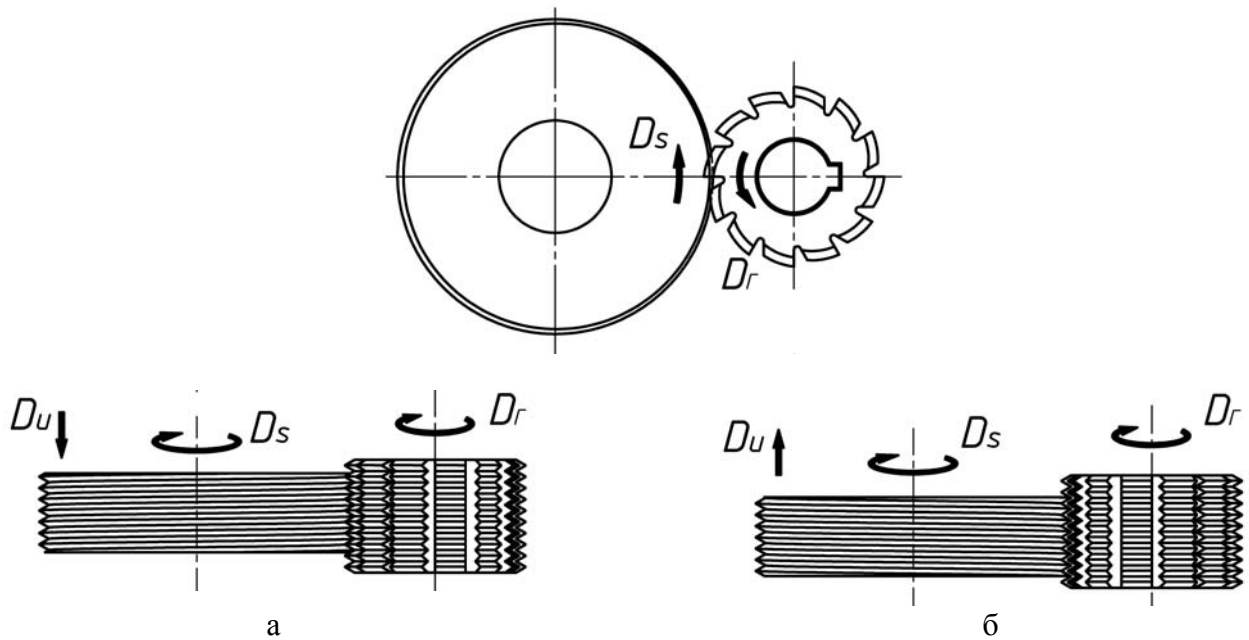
Фрезерование наружной резьбы: а – правая резьба, б – левая резьба.
